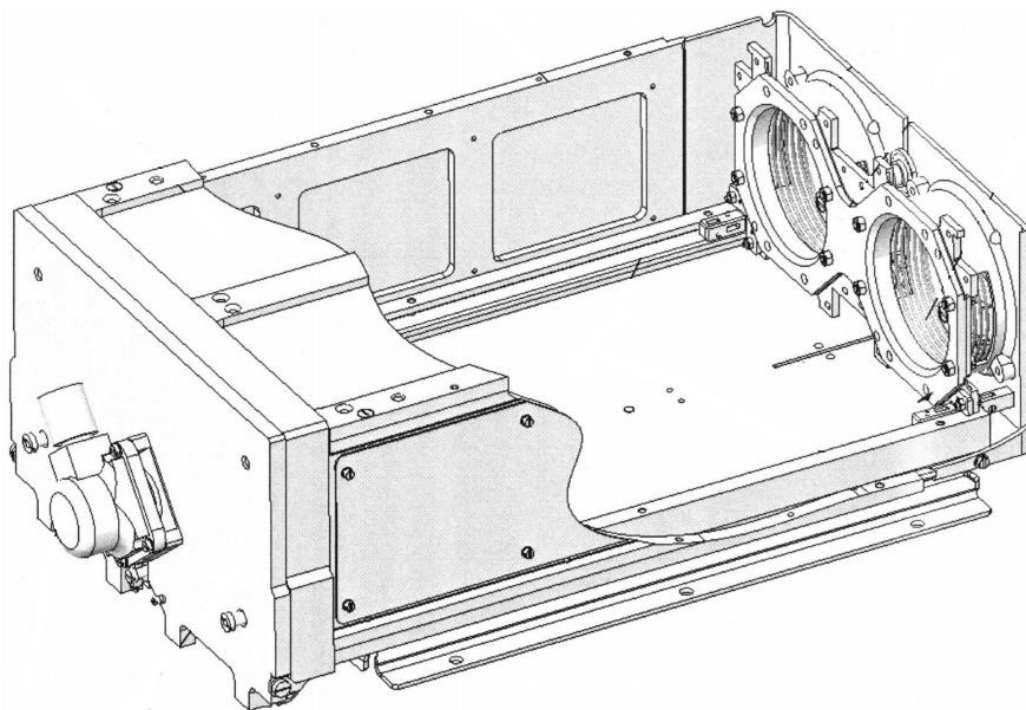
Общий вид ТПК. Конфигурация для запуска МКА формата 6U использующего две направляющие
